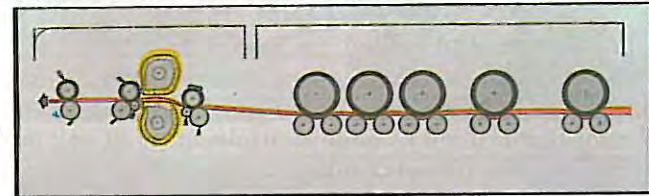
SC400 çekme makinasının çalışma kesit diyagramı
